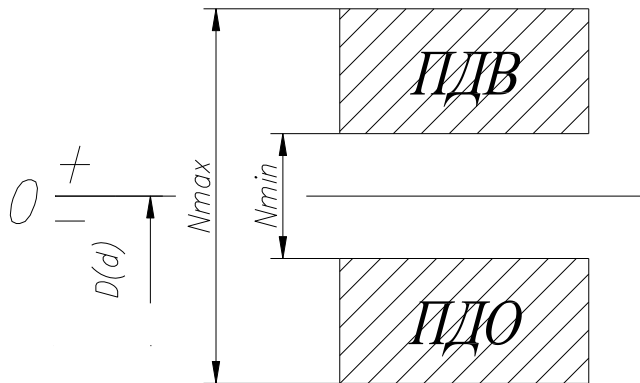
Схема розташування полів допусків з'єднання з натягом
